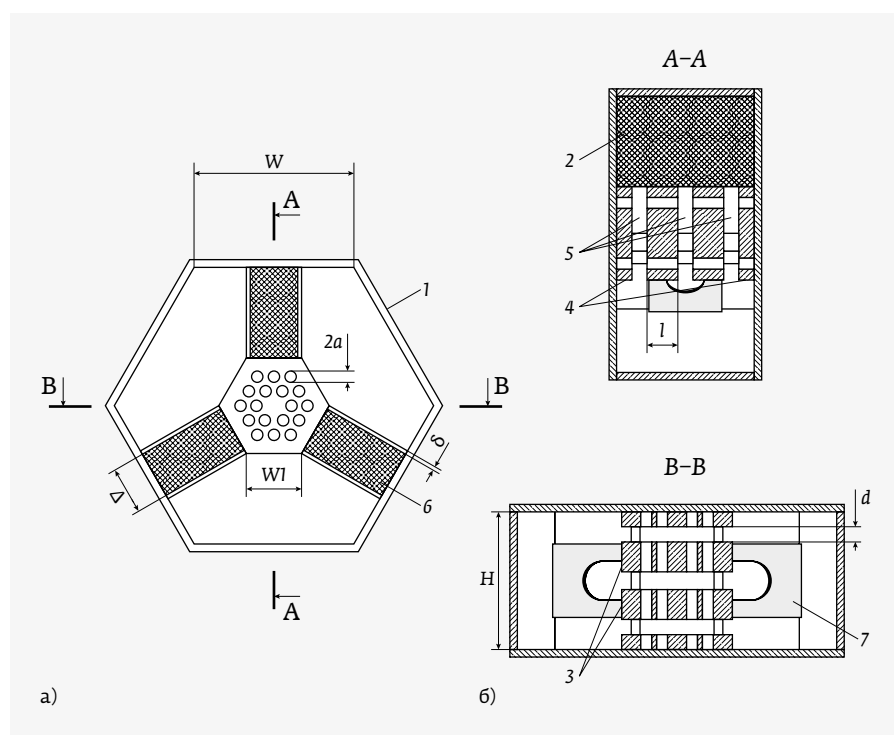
Конструкция резонатора: а – вид сбоку на резонатор со снятой боковой крышкой; б – поперечное сечение резонатора
